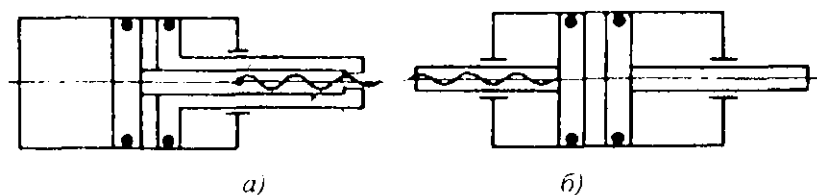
Схема цилиндра: а – с раздвижными полупоршнями; б – с перемещением встроенного в цилиндр фланца
